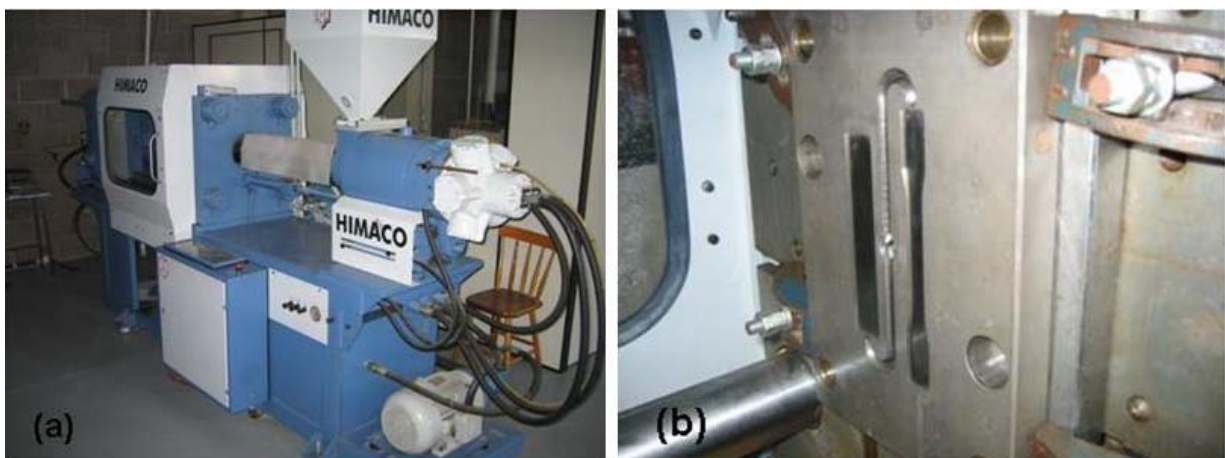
Equipamentos utilizados: (a) Máquina injetora; (b) molde dos corpos de prova
